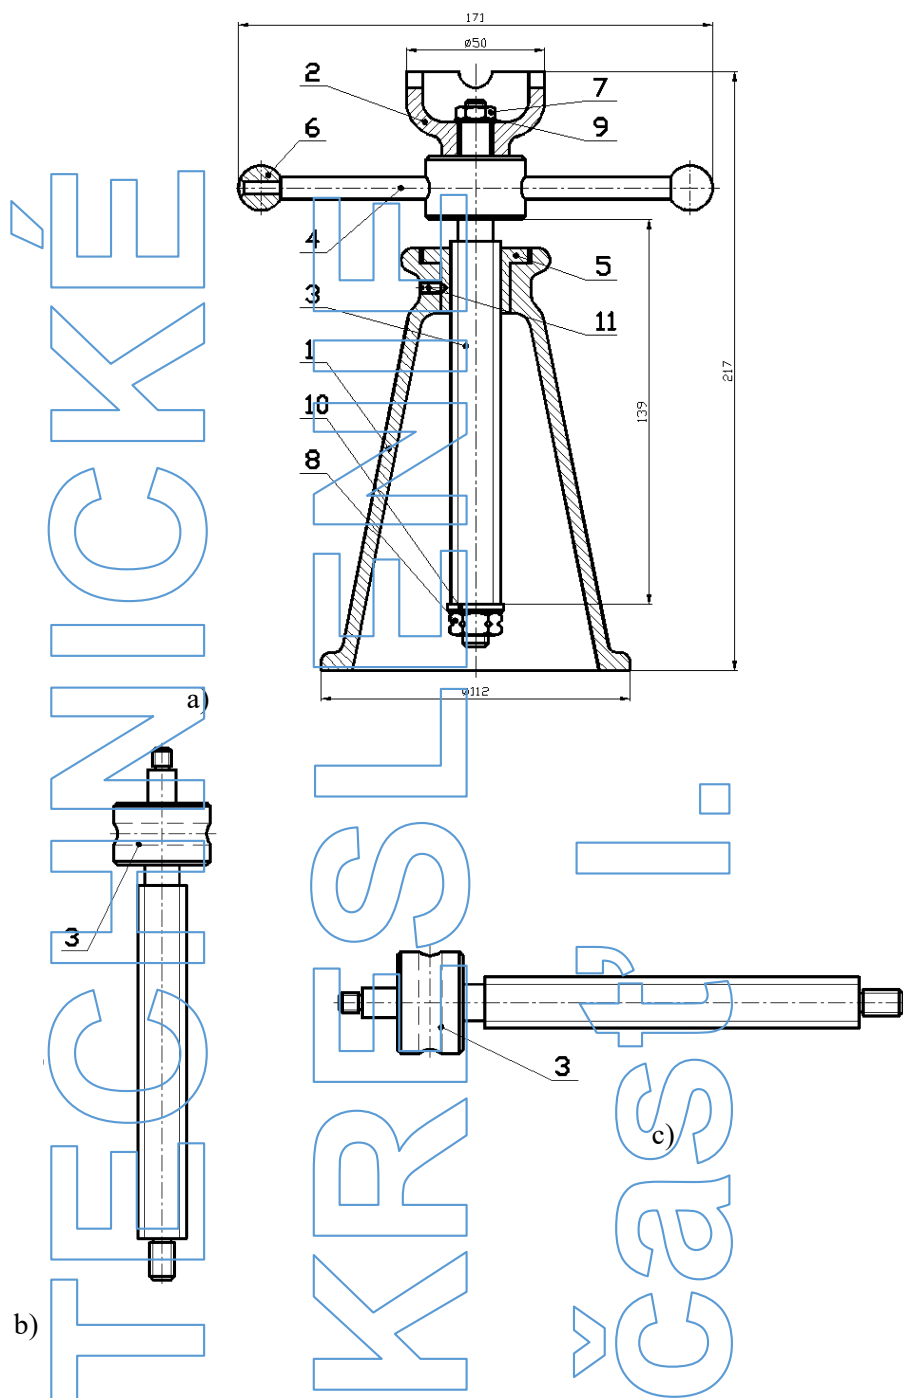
Umiestnenie pohľadov pri zobrazovaní v pomocou premietania v 3. kvadrante
